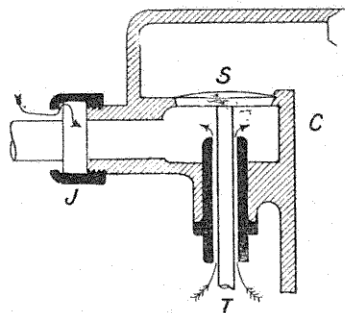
Aspiration d'air par la tige T de la soupape S et le joint J de la tuyauterie.
